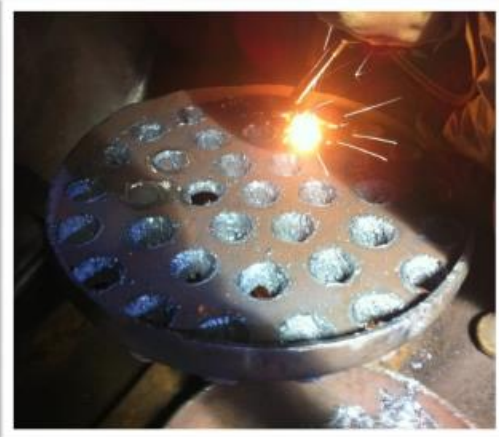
Antes del desboquillado      Figura 9.12 Desboquillado soporte
